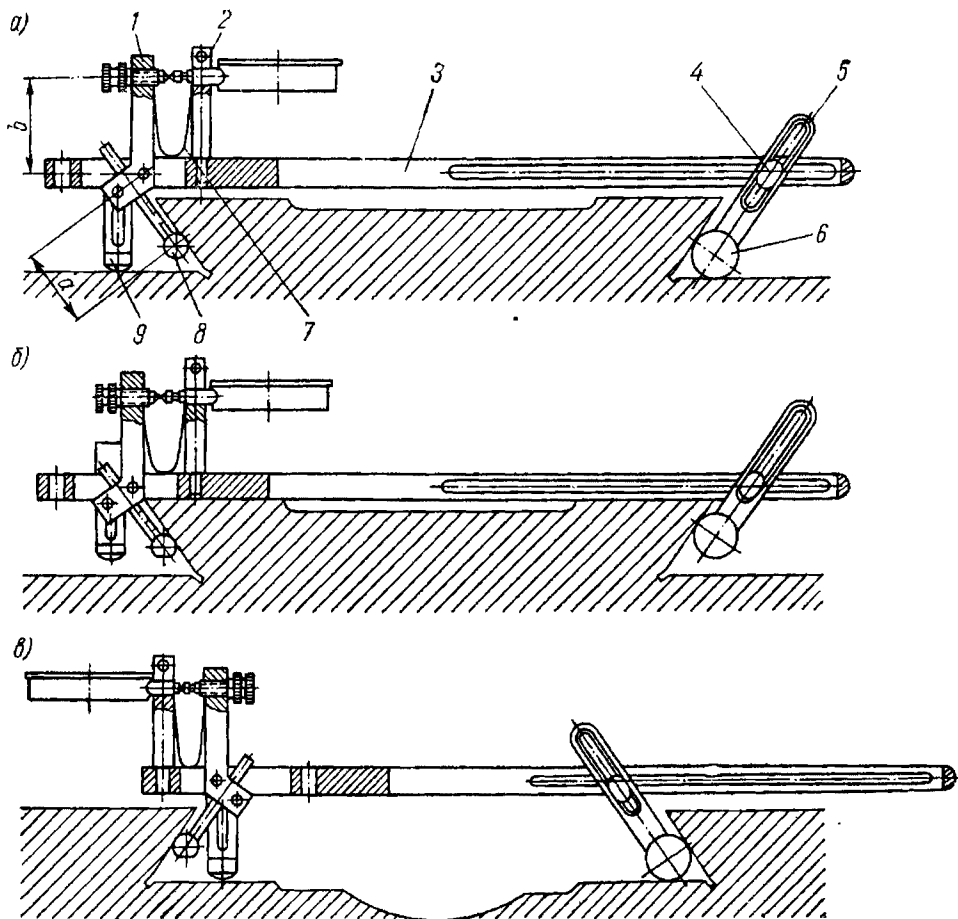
Приспособление для проверки параллельности направляющих формы «ласточкин хвост»
